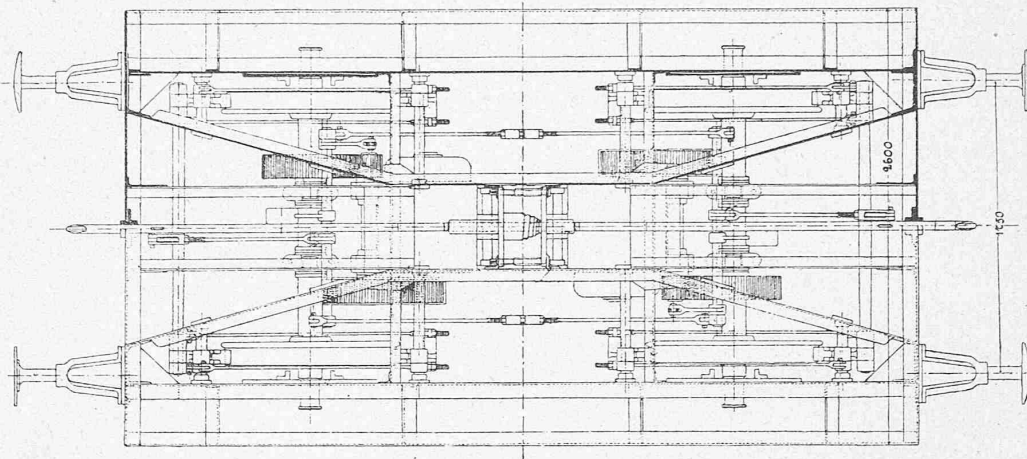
Grundriss; Masstab 1 : 40.
